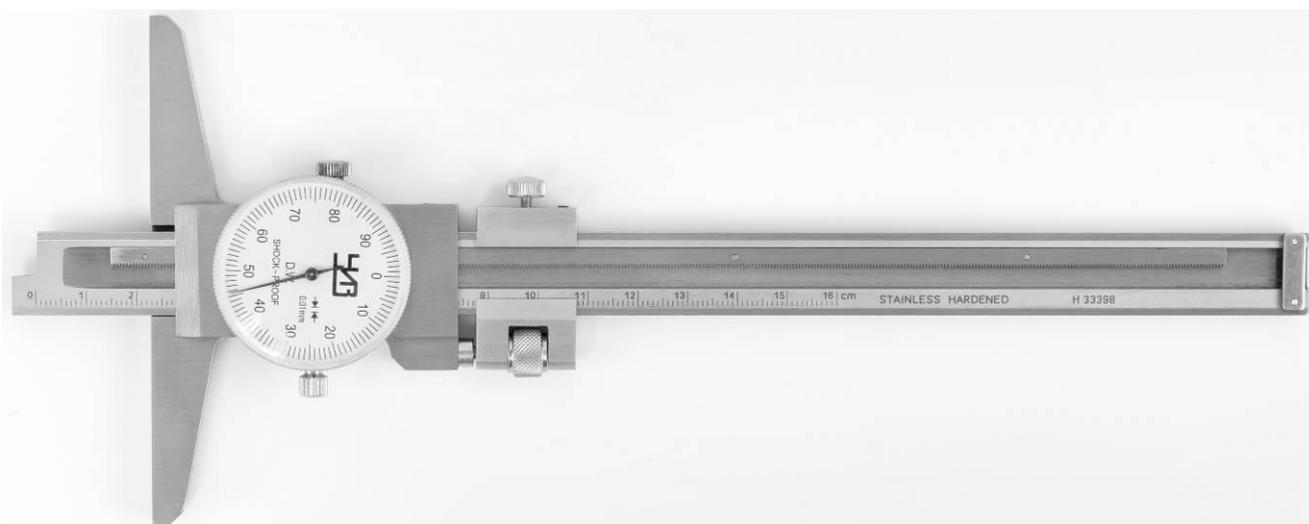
Общий вид штангенглубиномеров модификации ШГК со ступенчатым торцом штанги
